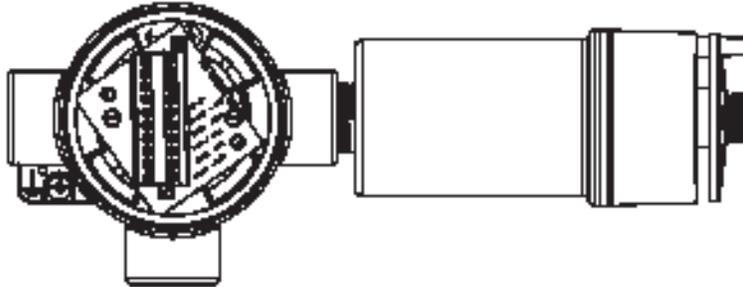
Modelo de sensor remoto XIR a prueba de explosión/ignífugo
